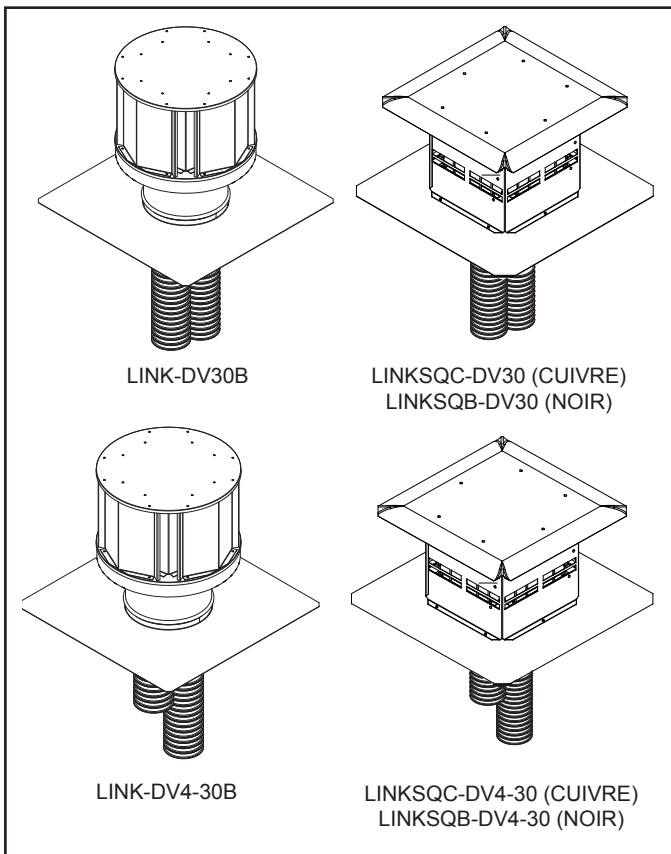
Ensembles de doublage de conduit flexible d'évacuation directe
